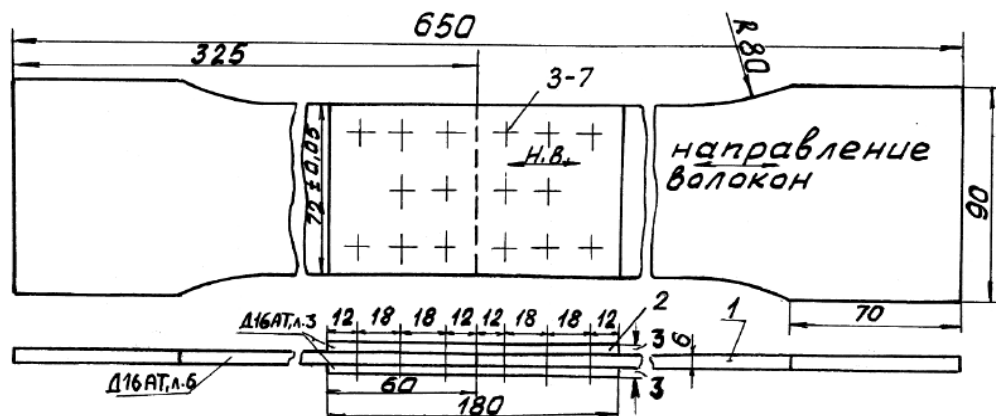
Образец поперечного многоточечного двухсреznego болт-заклепочного стыкового соединения из сплава Д16АТ
